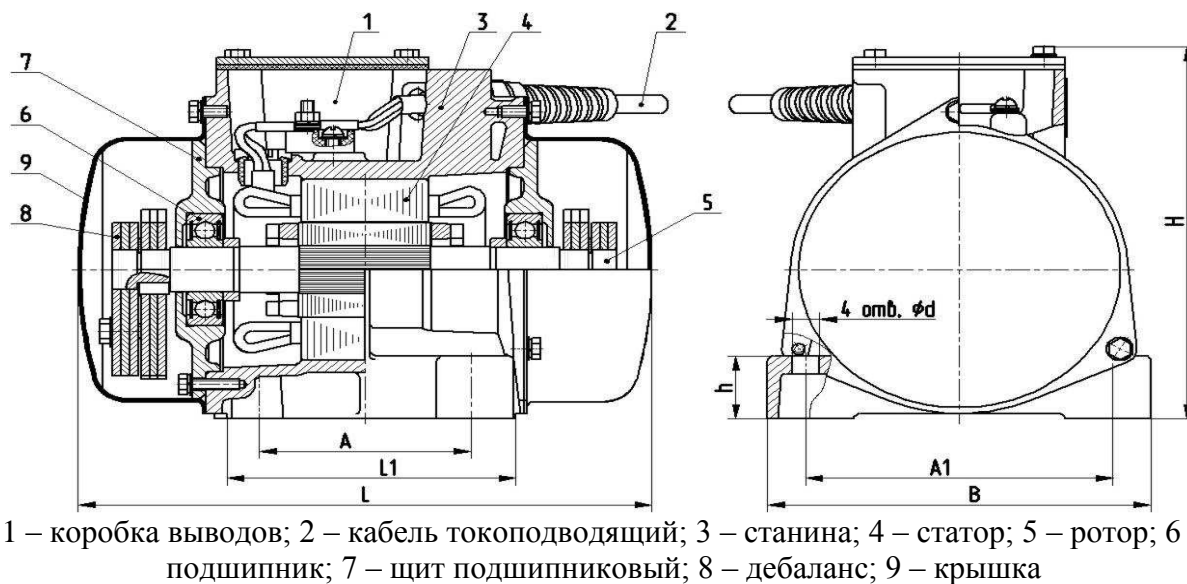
Общий вид электромеханического вибратора общего назначения с круговыми колебаниями ИВ-99Б
